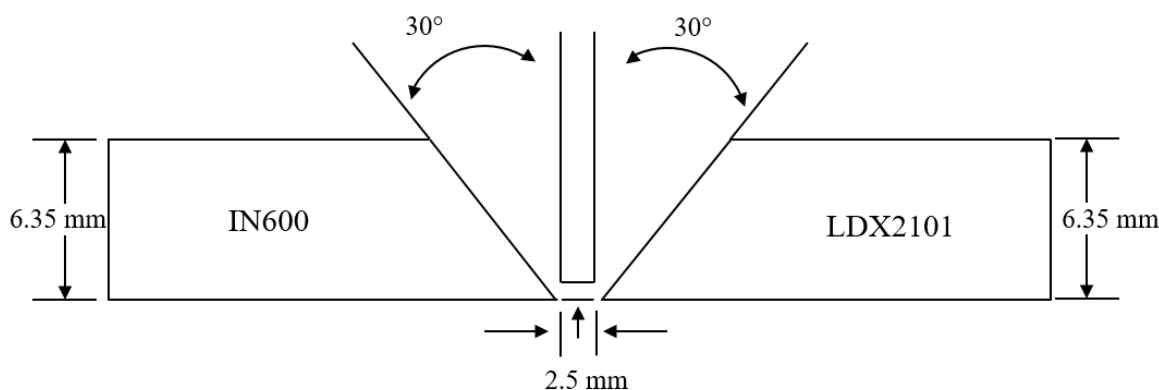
Diseño y dimensiones de la junta soldada disímil, cotas en mm.
